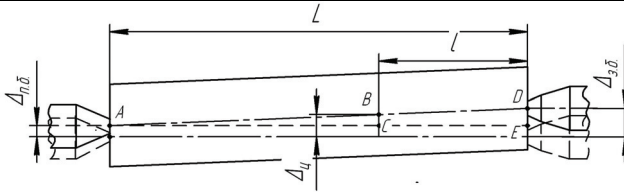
Схема формування похибки обробки від впливу пружних деформацій передньої і задньої бабки
